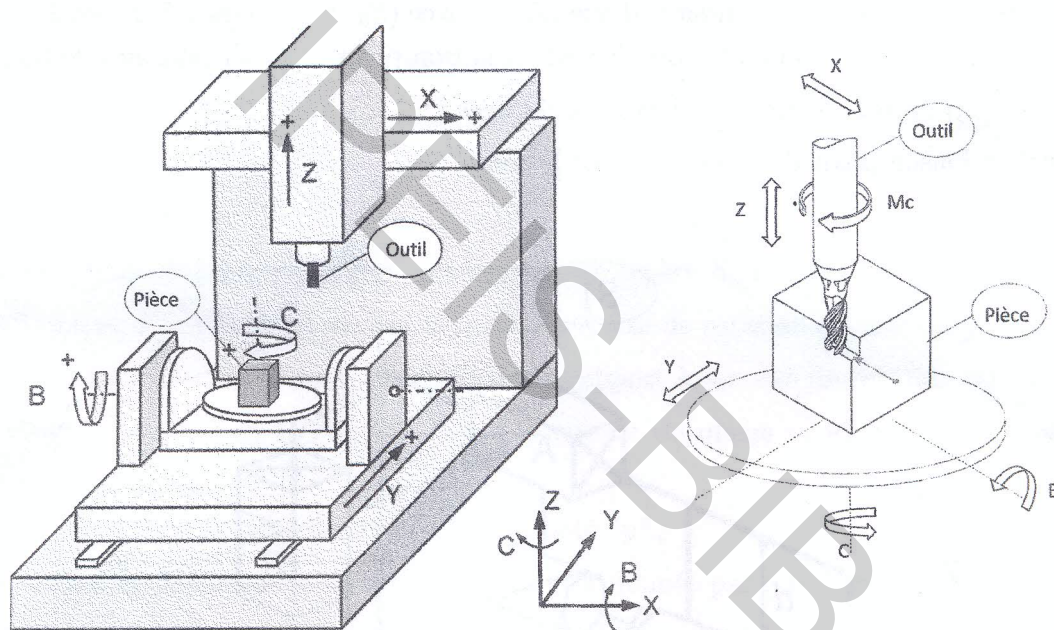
Vue globale du centre d'usinage avec repérage des « axes »
